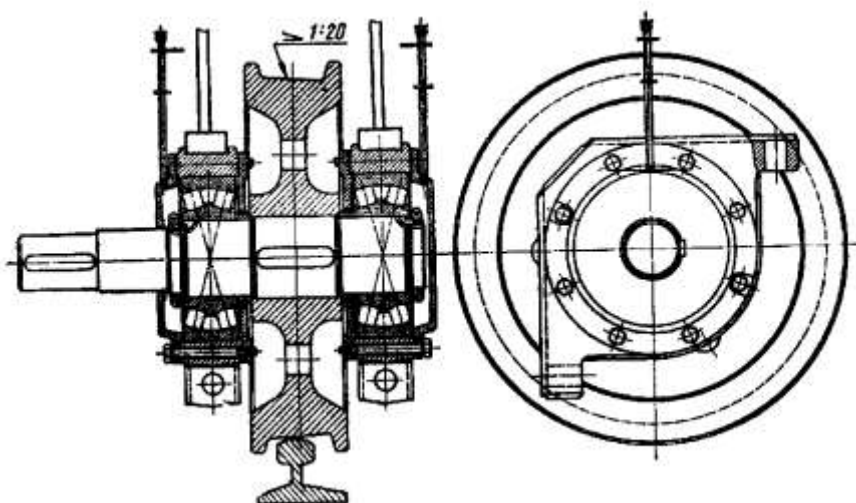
Схема установки ходового колеса с конической поверхностью катания на сферических роликовых подшипниках
